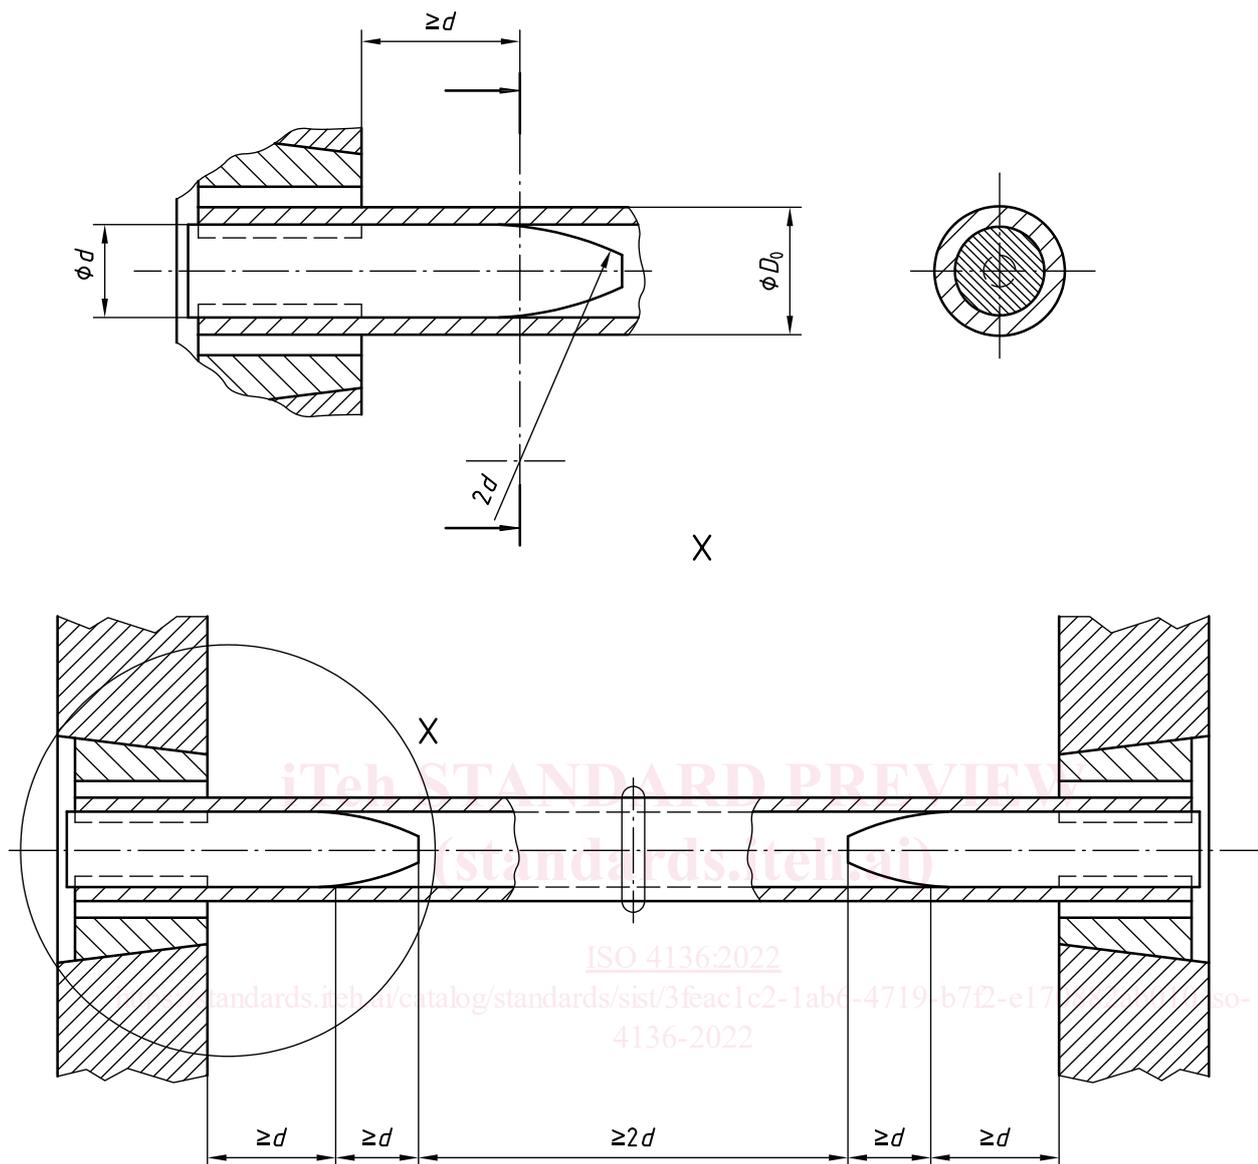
Éprouvette de traction pour tube soumis à essai sur toute sa section
